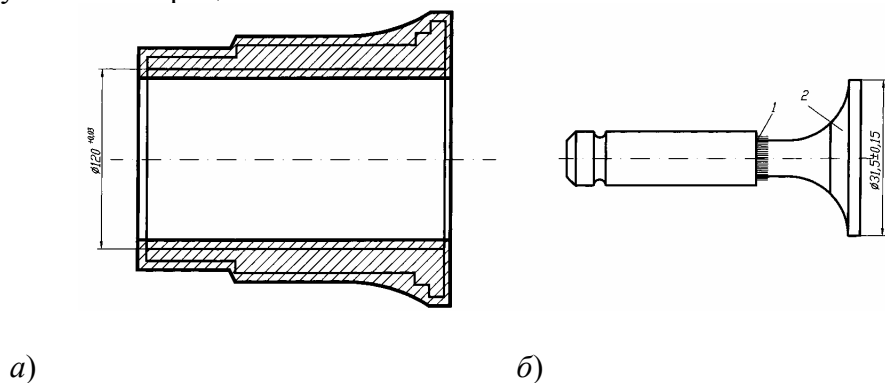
Заготовки для гильзы цилиндра (а) и для клапана сварной конструкции (б):
